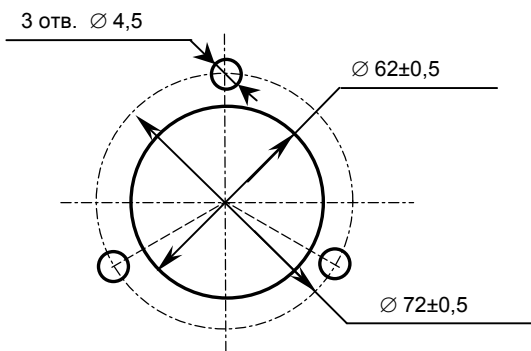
Установочные размеры штурвала LGF-12-003B-100
